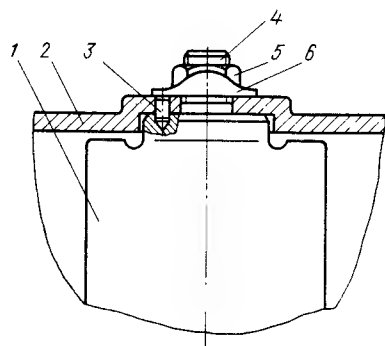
Крепление лопатки к корпусу с помощью резьбовой цапфы: 1 — лопатка направляющего аппарата; 2 — корпус; 3 — штифт, фиксирующий положение лопатки относительно корпуса; 4 — цапфа с резьбой; 5 — гайка; 6 — контровка
